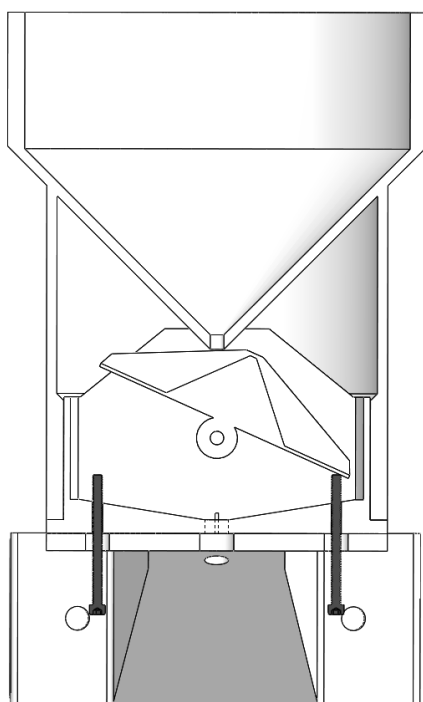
Render mechanismu srážkoměru ze strany pro montáž hallova senzoru
